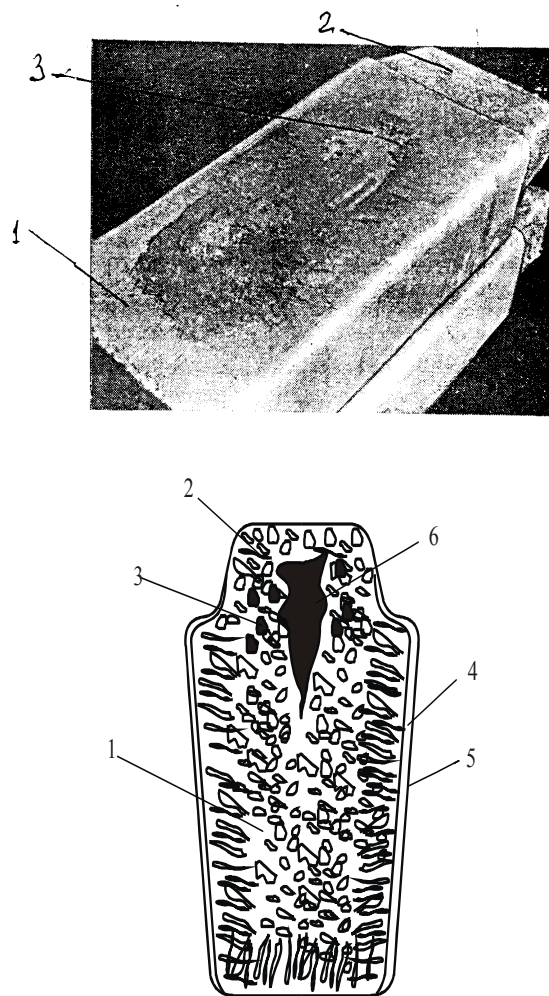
Загальний вигляд (а) та кристалічний злом (б) зливка спокійної сталі 12Х18Н10Т масою 12т: 1 - тіло зливка; 2 - прибуткова частина; 3 - включення і плівки; 4 - кірка; 5 - дендритні кристали; 6 - усадочна раковина.
